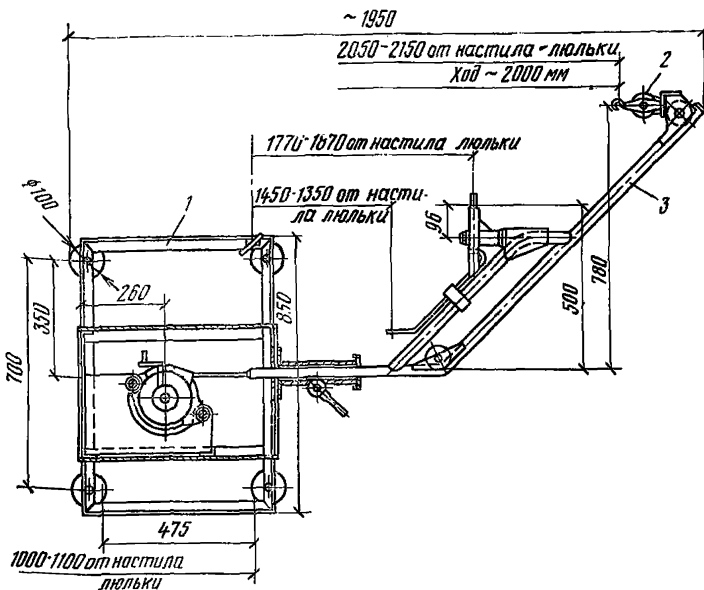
Приспособление для работы с механизированным инструментом (каретка) конструкции ПКБ ЛНИИ АКХ
